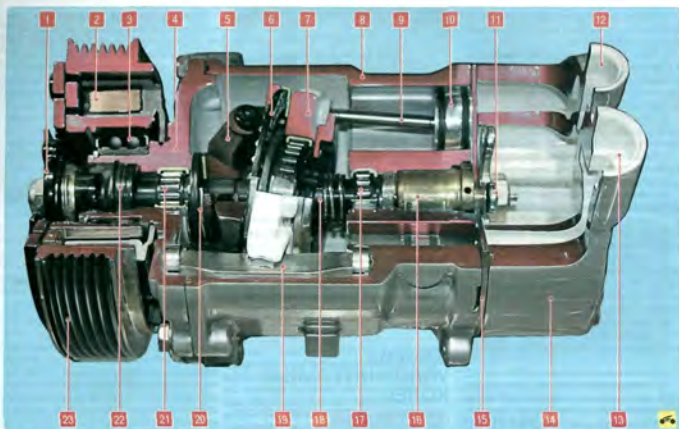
Компрессор кондиционера: 1 – прижимной диск; 2 – обмотка электромагнита; 3 – подшипник шкива; 4 – передняя крышка корпуса; 5 – рычаг; обоймы наклонной шайбы; 6 – упорный роликовый подшипник наклонной шайбы; 7 – наклонная шайба; 8 – корпус компрессора; 9 – шатун; 10 – поршени; 11 – гайка крепления блока клапанов регулятора и упоров блока лестцевых клапанов; 12 – штуцер линии нагнетания; 13 – штуцер линии всасывания; 14 – крышка блока клапанов; 15 – блок лестцевых клапанов; 16 – блок клапанов регулятора производительности; 17, 21 – подшипники вала; 18 – вал наклонной шайбы; 19 – направляющий упор наклонной шайбы; 20 – упорный подшипник вала; 22 – сальник вала; 23 – шкив привода
